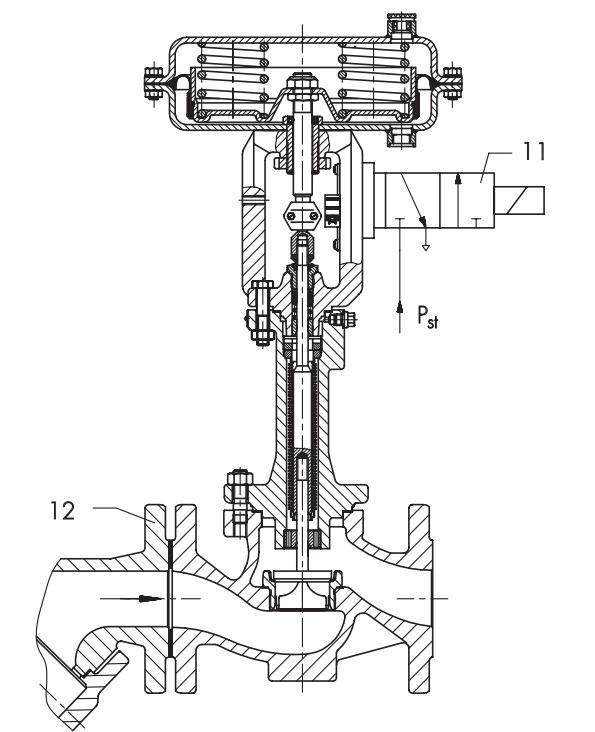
· Пневматический регулирующий и быстро закрывающийся клапан тип 241-1-газ
